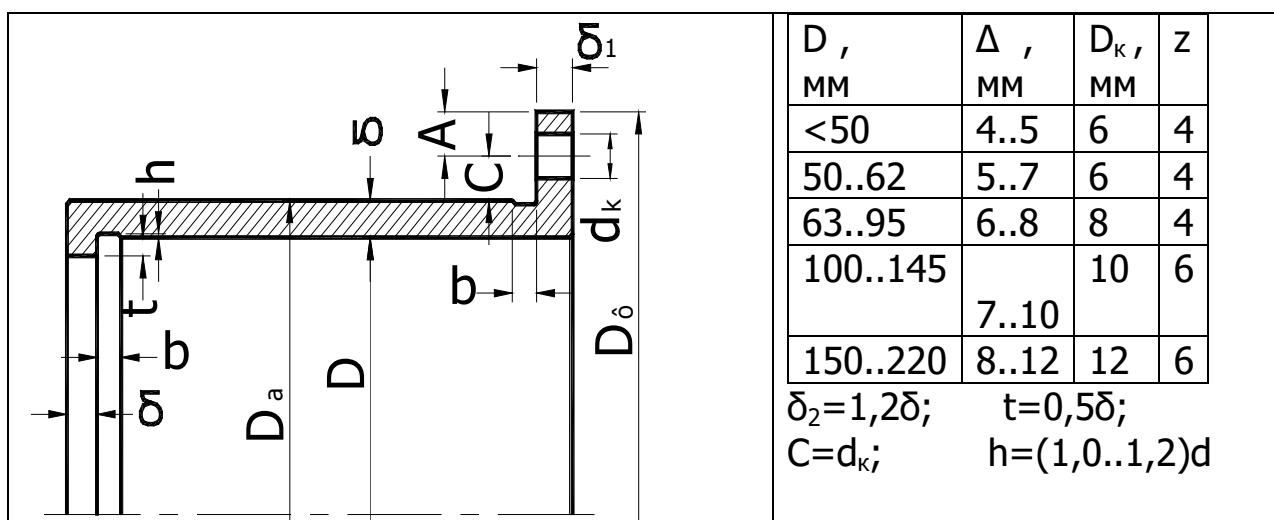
Стакан для установки фиксирующей опоры червяка на двух подшипниках. Толщина стенки δ , диаметр $d_{\text{к}}$ и число z крепежных винтов (болтов) от диаметра наружно кольца подшипника D . Посадки по D_a H7/k6 или H7/m6. Проточки для выхода резца на диаметрах D и D_a по ГОСТ8820-69; для компоновки ширина канавки $b=5$ мм, глубина $h=1$ мм.
